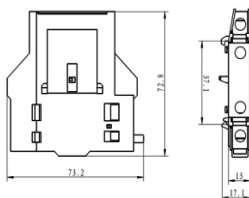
Габаритные и установочные размеры ПК03-01, мм.
